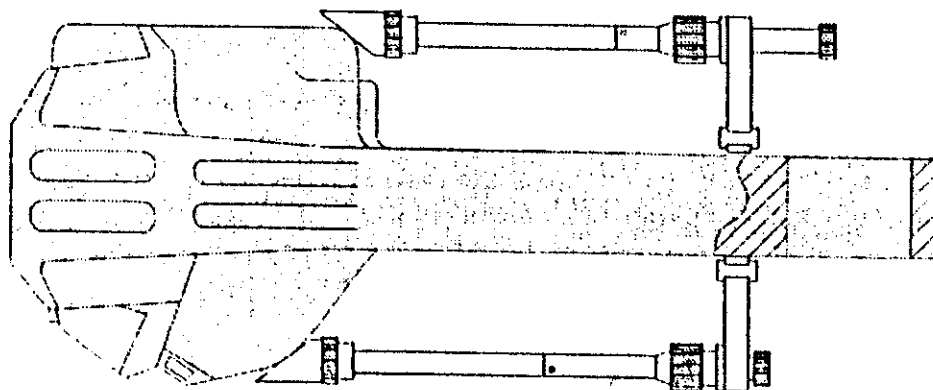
Намагничивание хвостовика корпуса автосцепки
